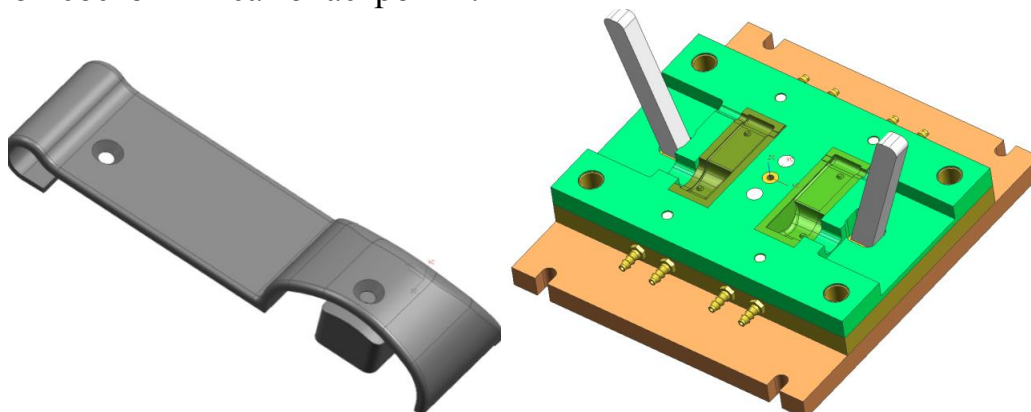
Деталь кассового аппарата и пресс-форма для её изготовления
